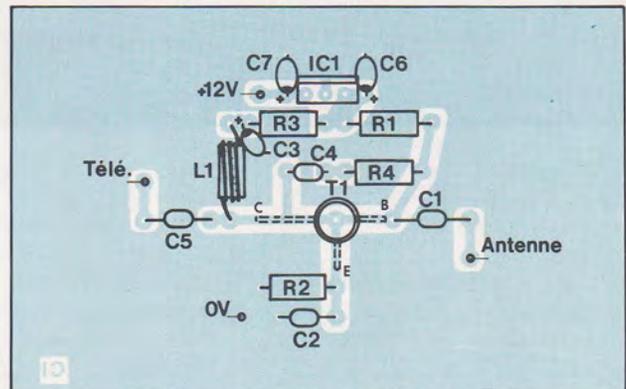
Le transistor BFR91 est soudé côté pistes.
